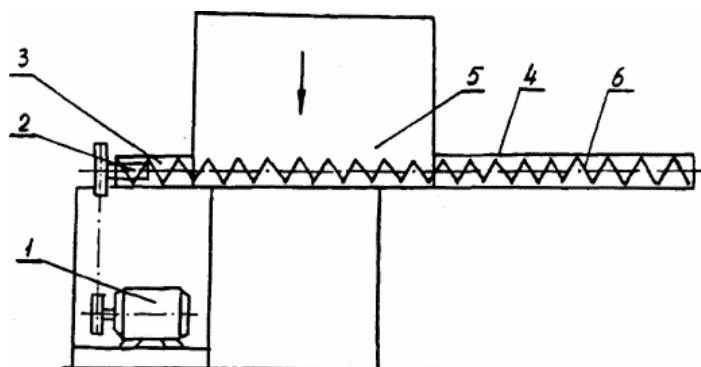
Пружинный транспортер для перемещения помета:
